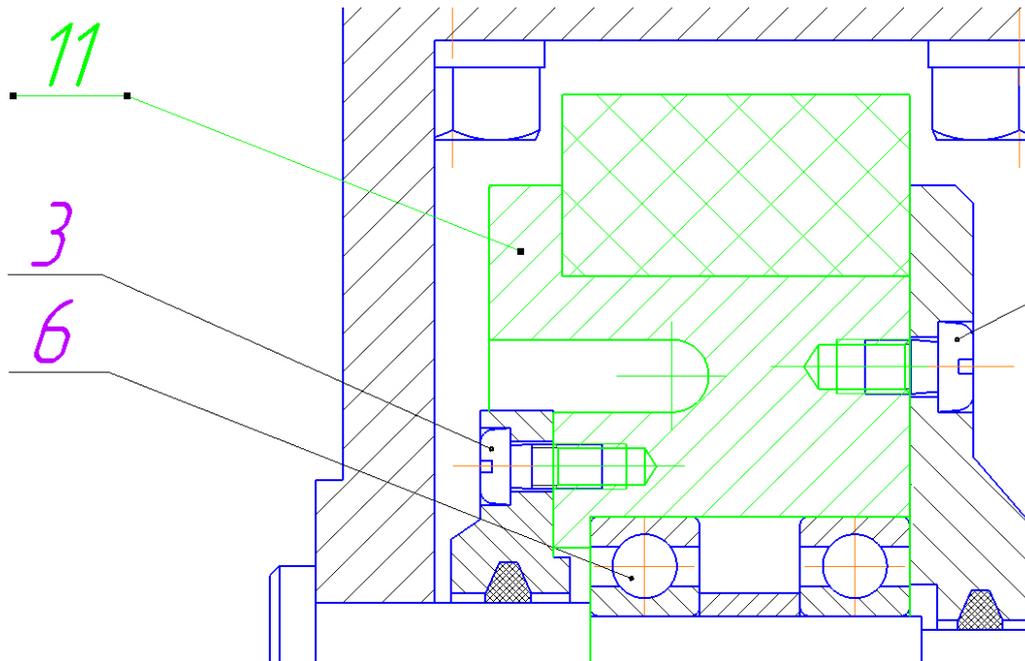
Простановка позиции к сборочной единице «Колесо»
